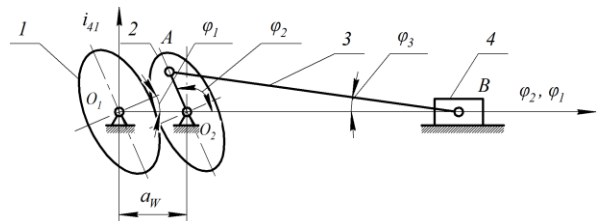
Кинематическая схема кривошипно-ползунного механизма с некруглыми зубчатыми колесами
